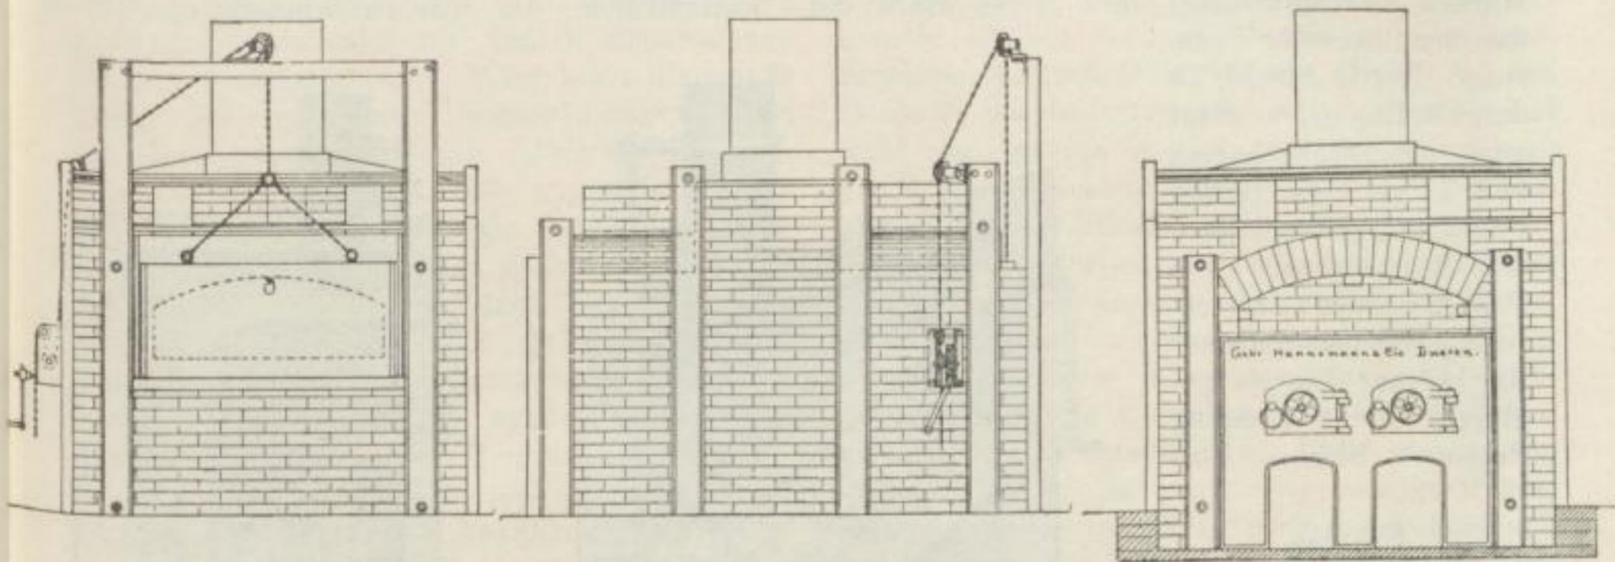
Ofen zum Oberflächenhärten von Geldschrankplatten.
